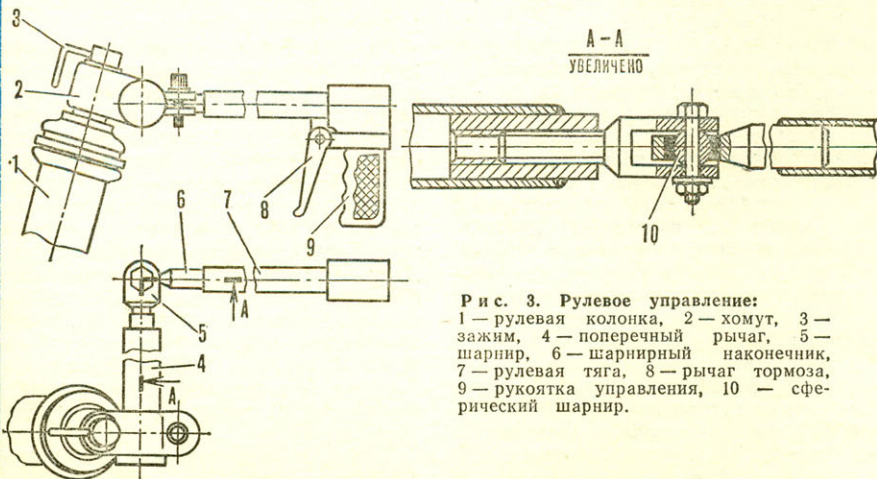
Рулевое управление: 1 — рулевая колонка, 2 — хомут, 3 — зажим, 4 — поперечный рычаг, 5 — шарнир, 6 — шарнирный наконечник, 7 — рулевая тяга, 8 — рычаг тормоза, 9 — рукоятка управления, 10 — сферический шарнир.
